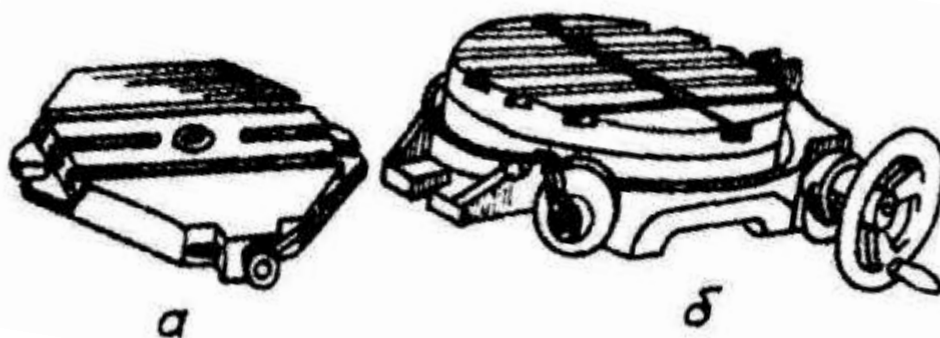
Неповоротный (а) и поворотный (б) столы
